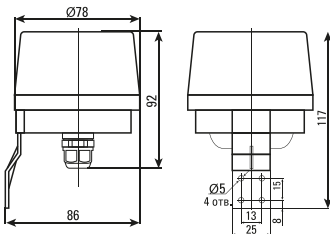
Габаритные и установочные размеры фотореле PS-4, PS-5
